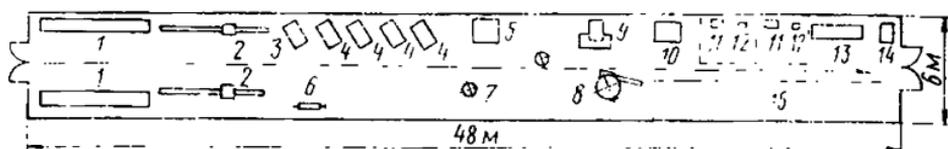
Схема прямолинейного технологического потока трубозаготовительного цеха
